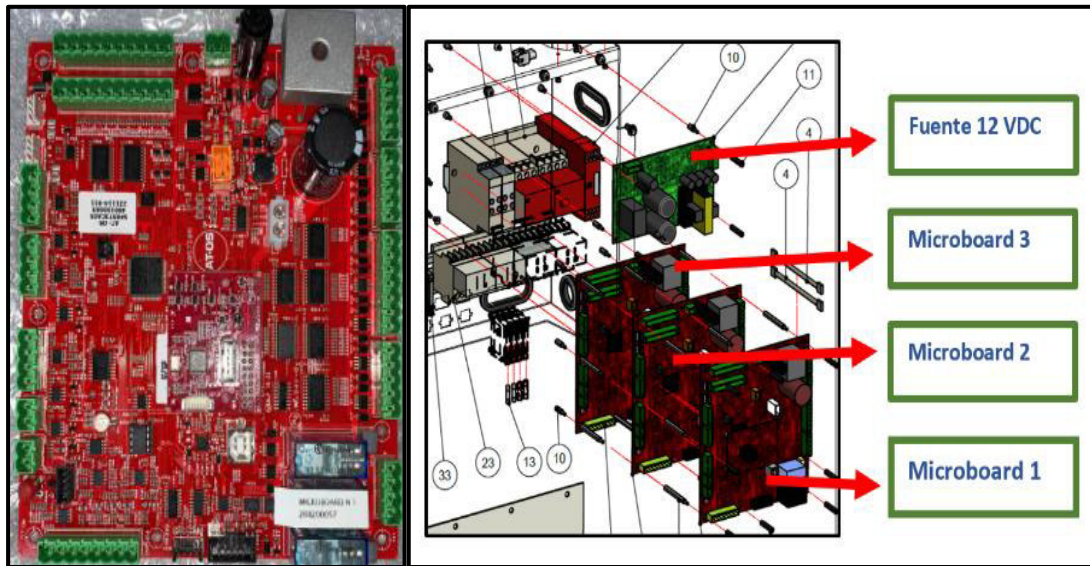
Placas de control principal y complementarias. Fuente: Datasheet Partes del Lavador - Tuttnauer
